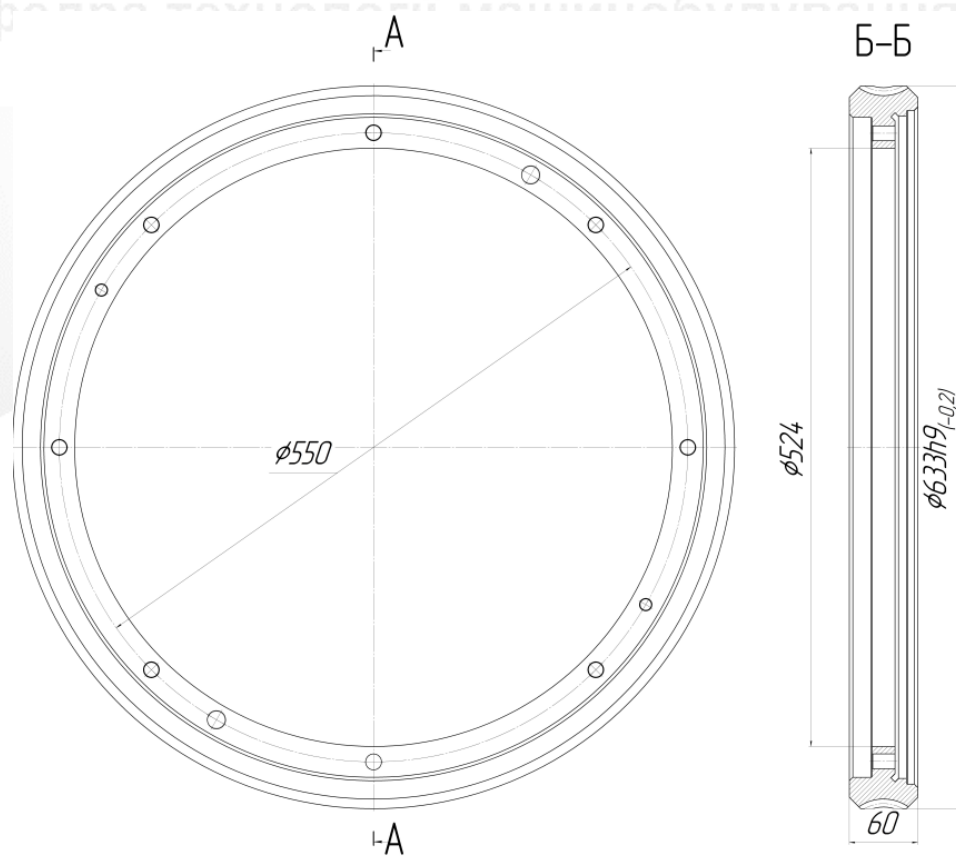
Ескіз деталі типу «Вінець червячного колеса»
